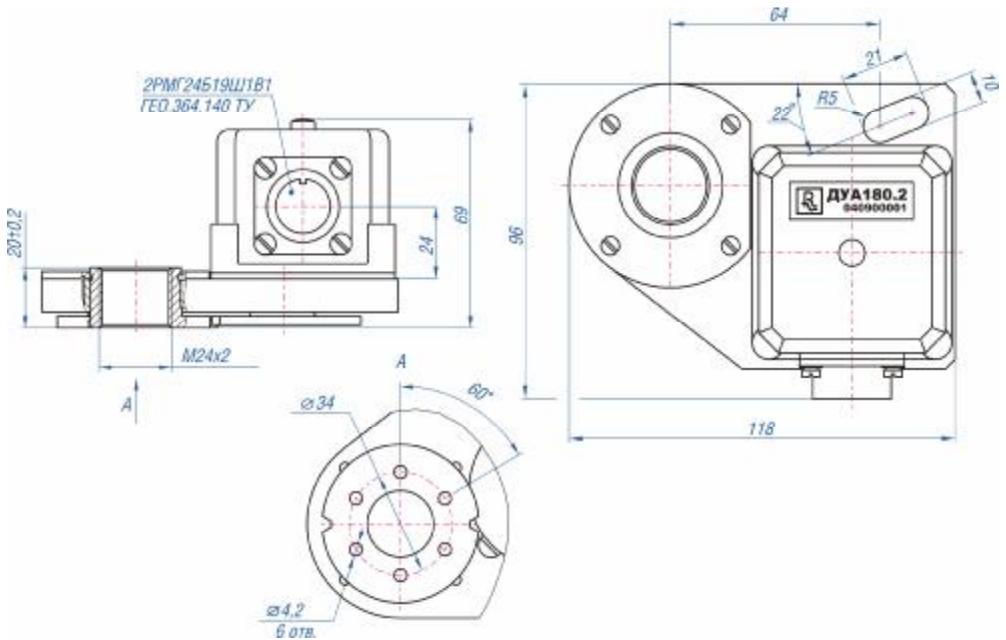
Габаритные и присоединительные размеры датчика азимута
